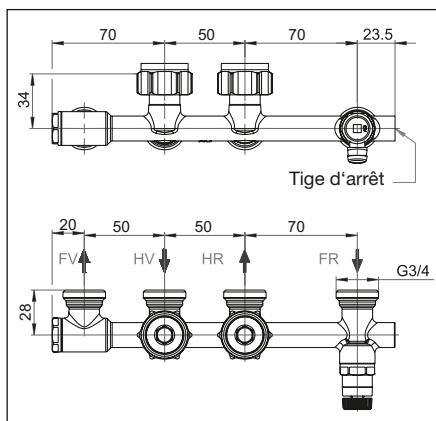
Dimensions ensemble de robinetterie pour la mise en service
